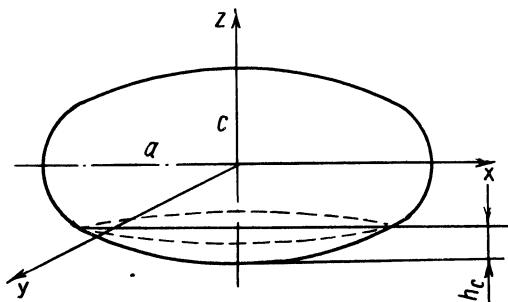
Схема внедрения абразивного зерна в поверхность детали
